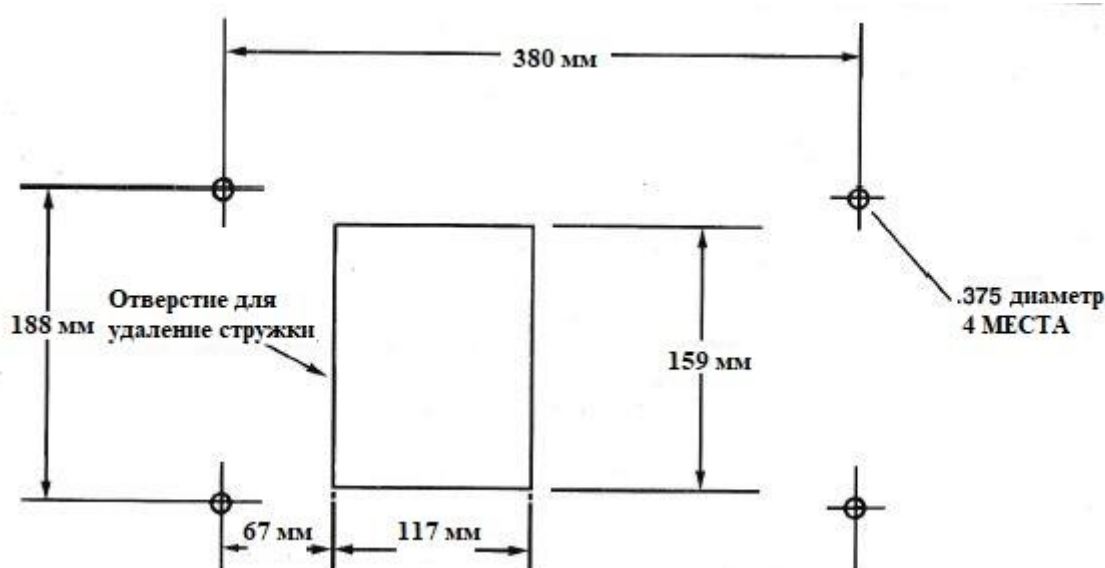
Размер и межцентровое расстояние отверстий на опорной поверхности
